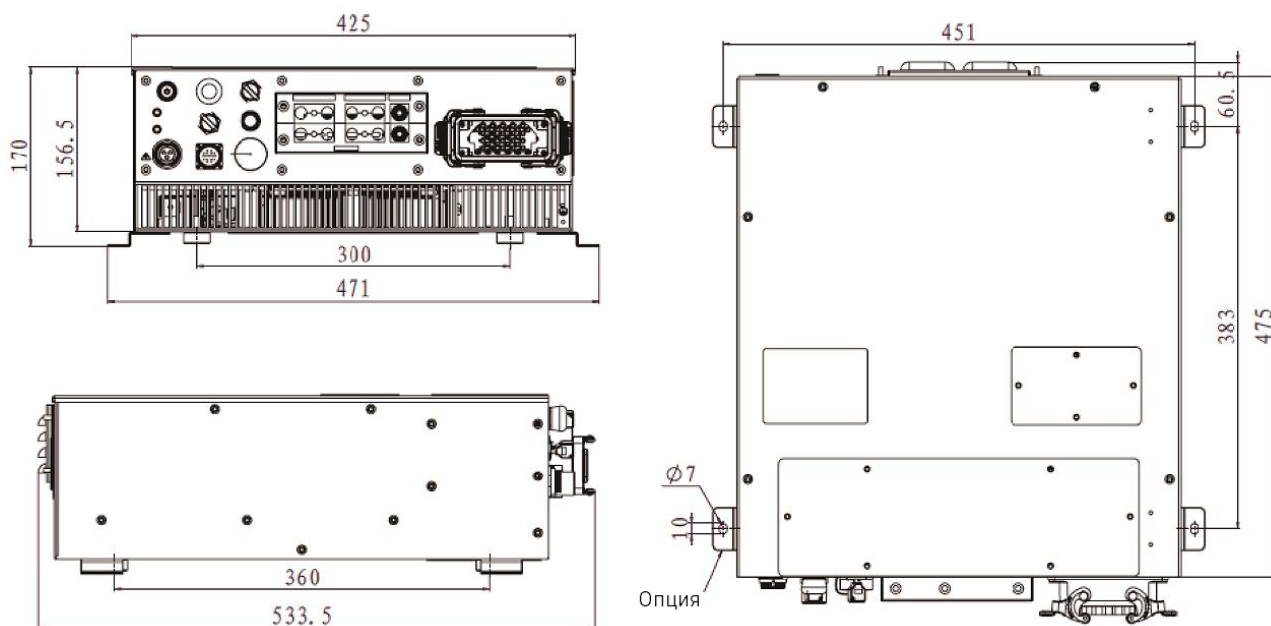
Размерный чертеж блока управления SRC4-S.
